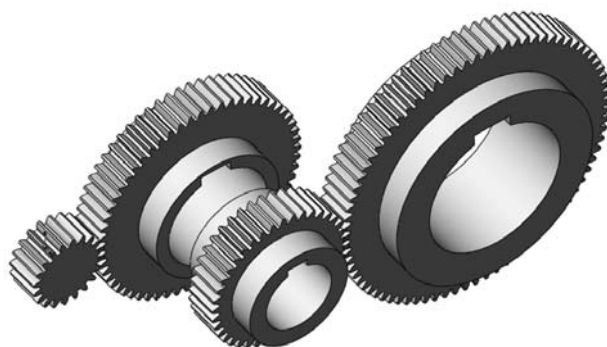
Изображение сборки колес зубчатого редуктора
